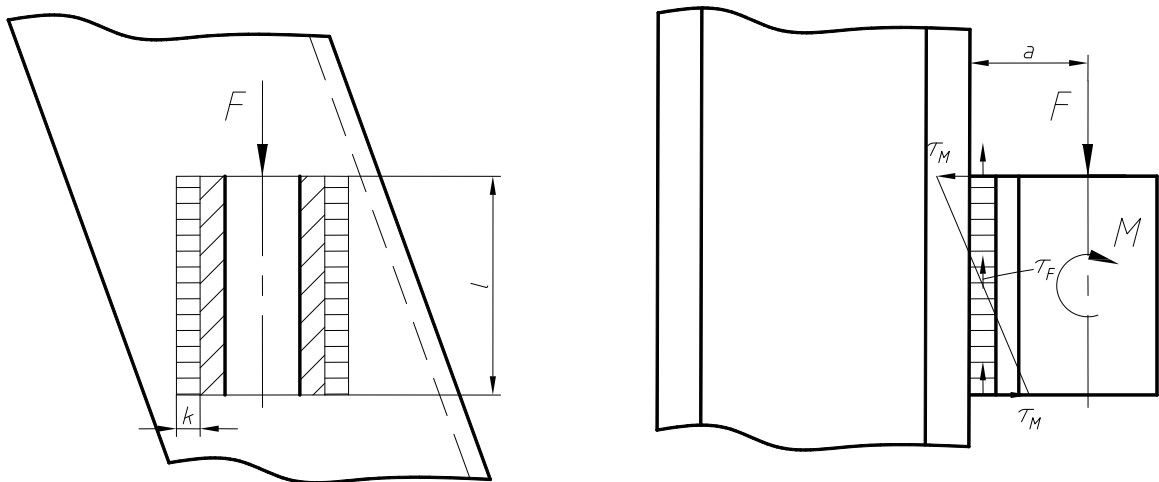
Зварне з'єднання кронштейна з корпусом
